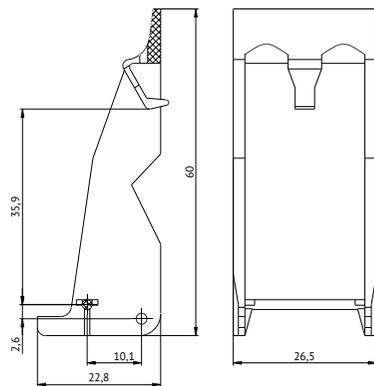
Габаритные, установочные присоединительные размеры фиксатора реле OptiRel 55-H4
